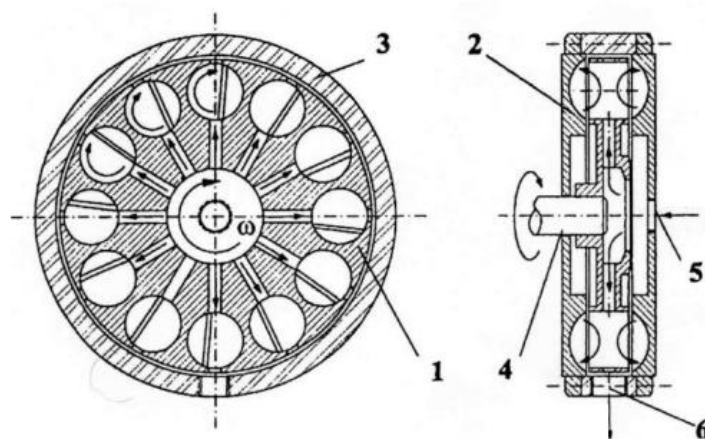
Схема гідродинамічного нагрівача ДДТУ: 1 – ротор; 2 – корпус; 3 – обід; 4 – вал приводу; 5 і 6 – вхід і вихід для молока
